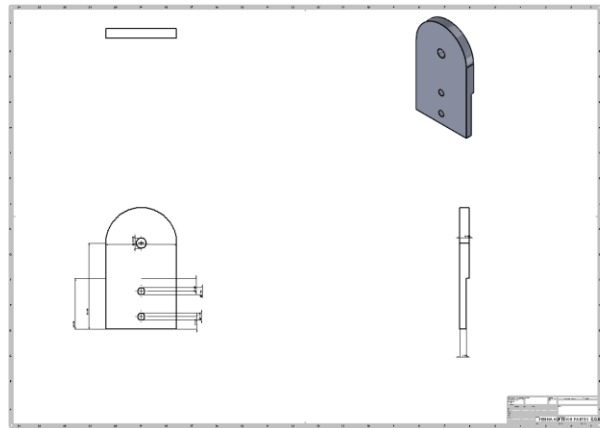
Perspectiva isométrica y vistas diédricas de la pieza 4.
